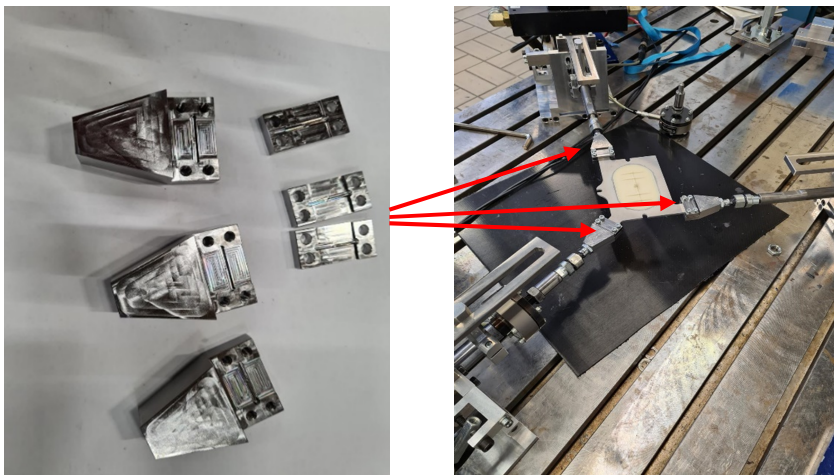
Spannadapter einzeln (li) und im eingebauten Zustand auf dem Prüfstand (re)
